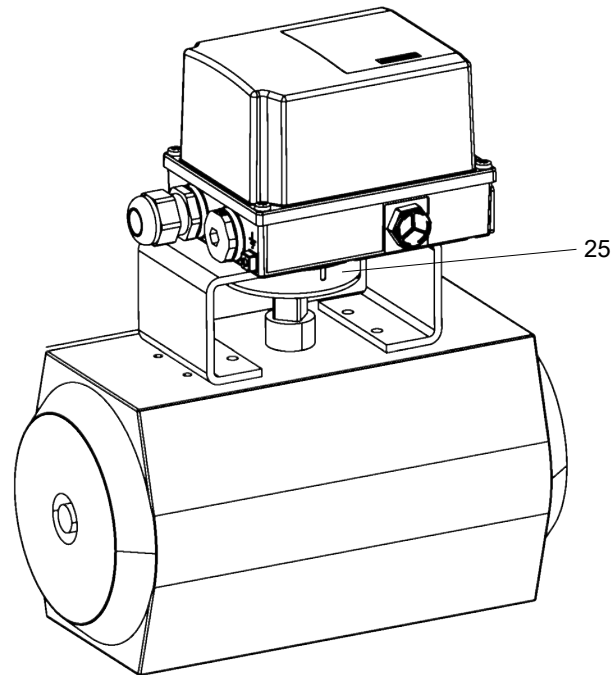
Stellungsregler mit Anbaukonsole angebaut am Schwenkantrieb
